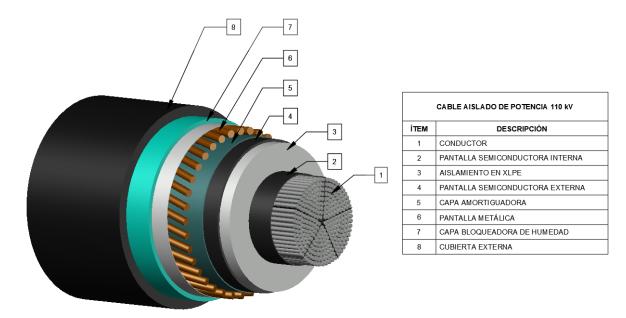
Corte longitudinal de los cables aislados de potencia
